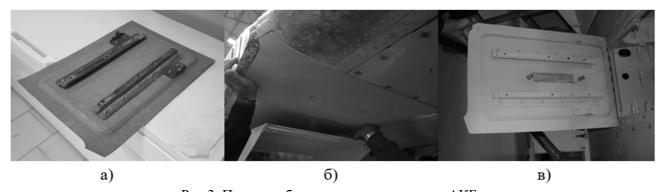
Процесс сборки и установки лючка АКБ: а) частично собранный неокрашенный лючок, б) предварительная установка детали, в) окончательная установка лючка на Миг-29 UPG
